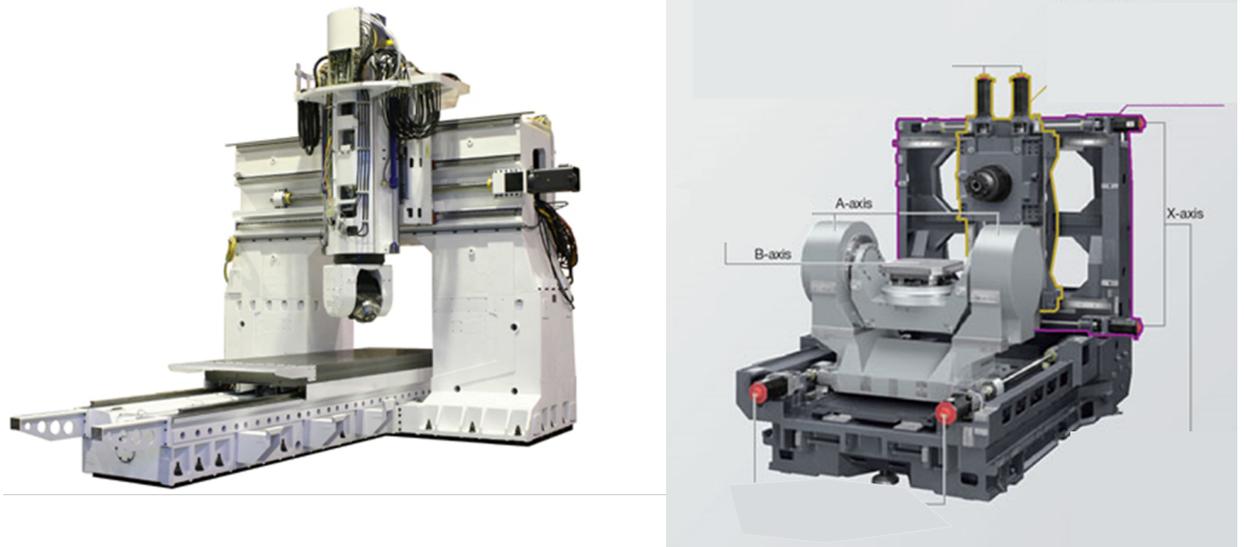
Exemplos de centros de usinagem com 5 eixos de diferentes configurações.
